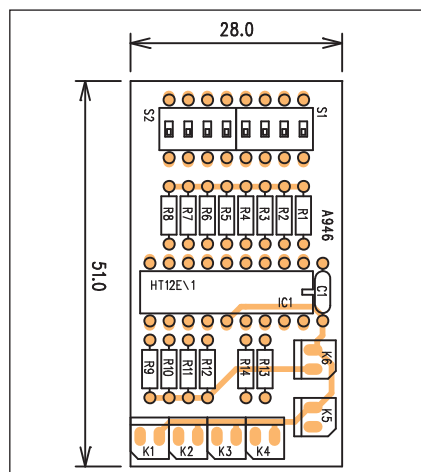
Obrazec desky spoju testeru (strana BOTTOM)
